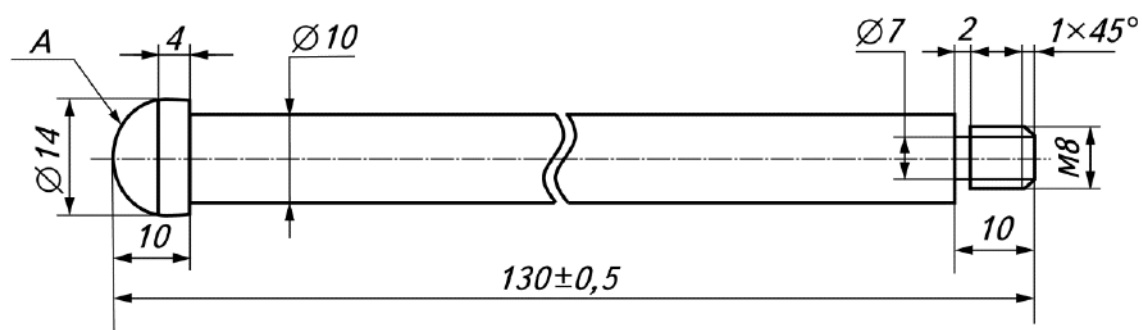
Рукоятка для винтового зажима столярного верстака
